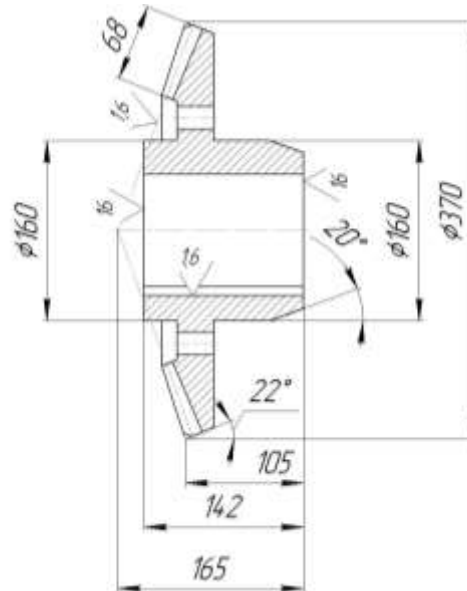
Зубчасте колесо редуктора типу КЦ1-400
